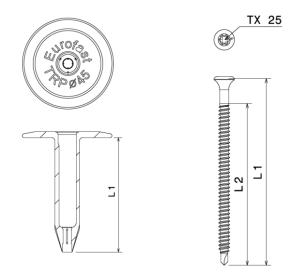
Vis EUROFAST EDS-B-4,8+ plaquette de fixation EUROFAST TRP-45
